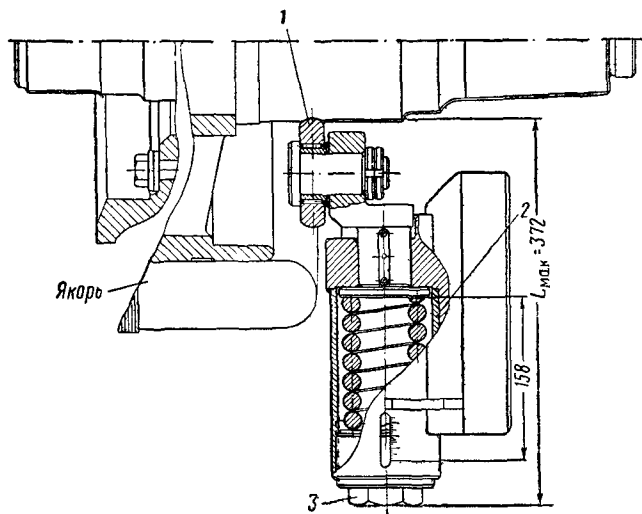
Приспособление для упрочнения накаткой валов тяговых двигателей:
